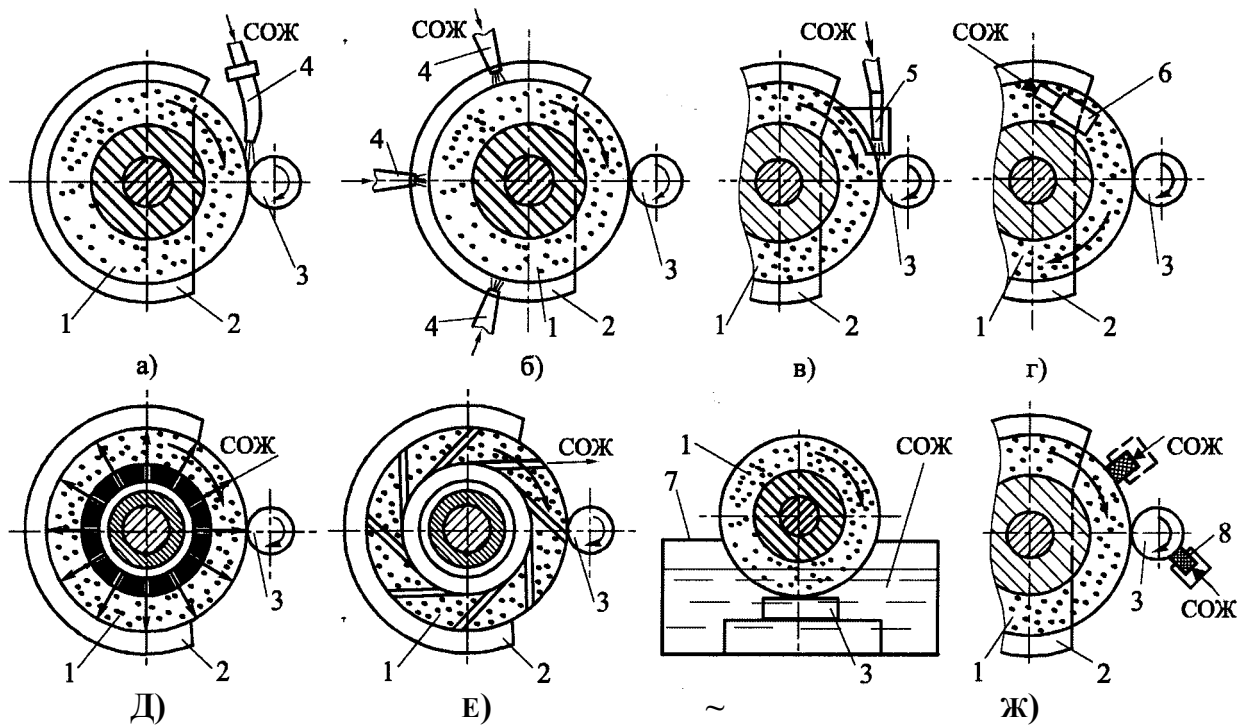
Схемы основных способов подачи СОЖ при шлифовании: 1 - шлифовальный круг; 2 - кожух; 3 - шлифуемая заготовка; 4 - сопло; 5 - насадок; 6 - торцовый насадок; 7 - емкость с СОЖ; 8 - мягкий пористый материал, пропитанный смазкой
